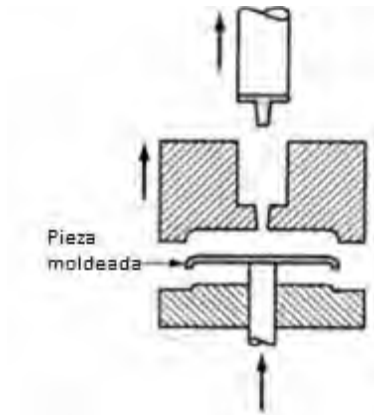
Pieza obtenida del moldeo por transferencia (Díaz, F., 2012).
